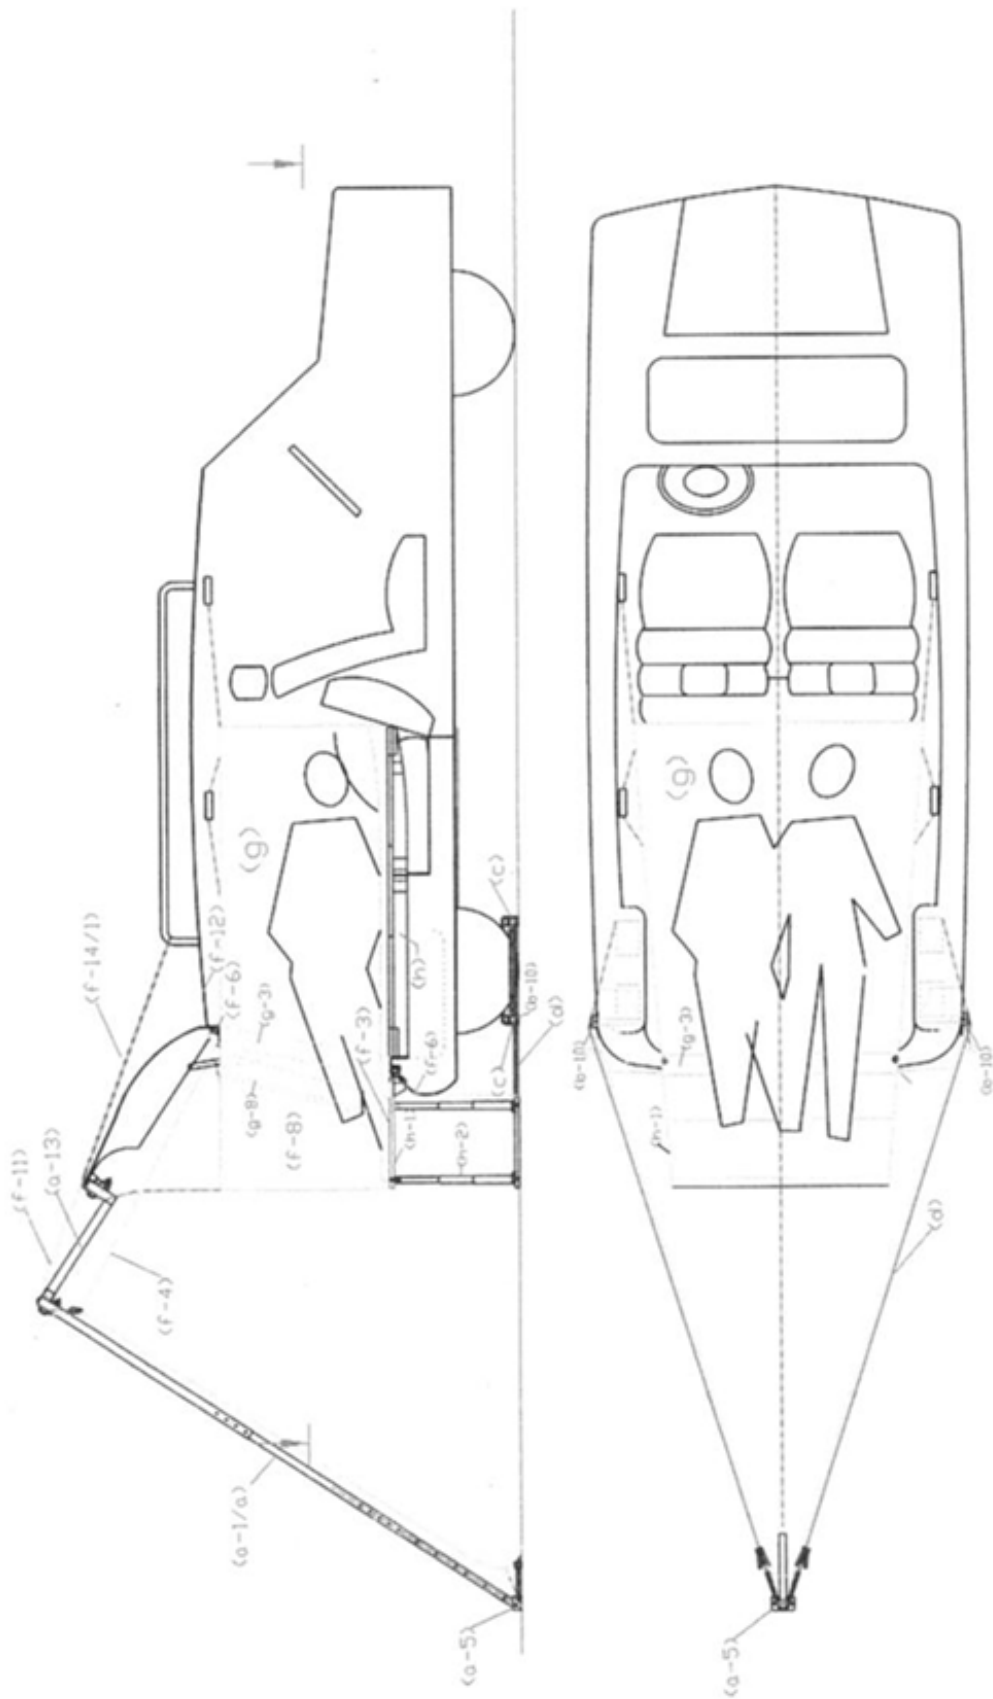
SEZIONE LONGITUDINALE E ORIZZONTALE AUTO
